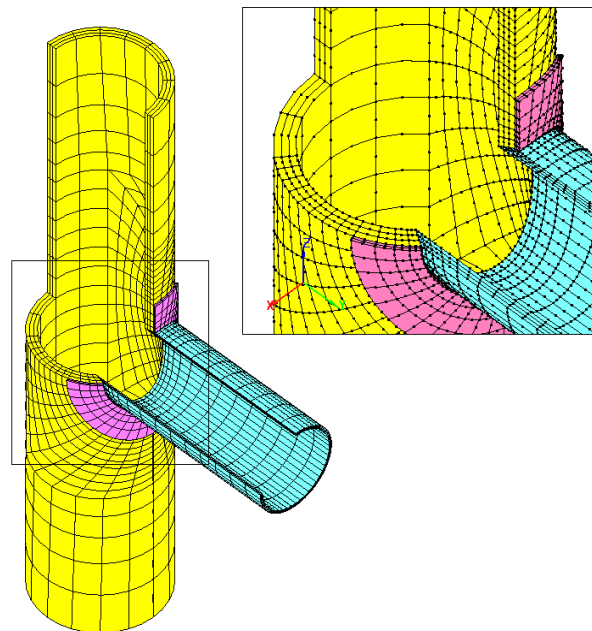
Тройник сварной с пропущенным штуцером.
